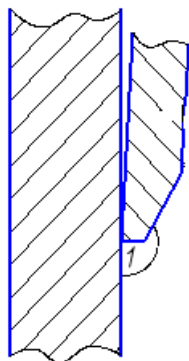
Базовая техника формирования сварного соединения
